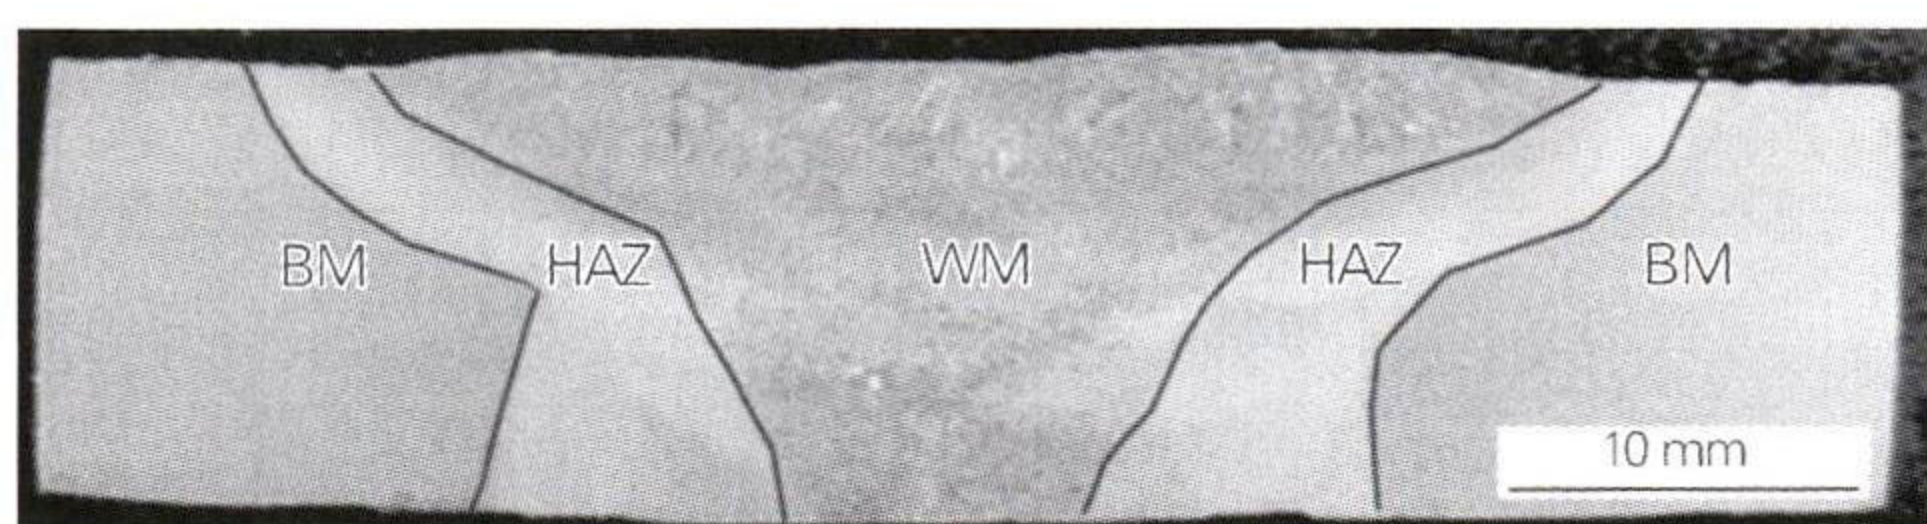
10Cr9Mo1VNb 钢热丝 TIG 焊接接头的宏观形貌
